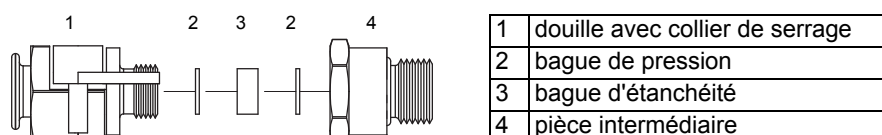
Presse-étoupe pour exploitation minière M25
